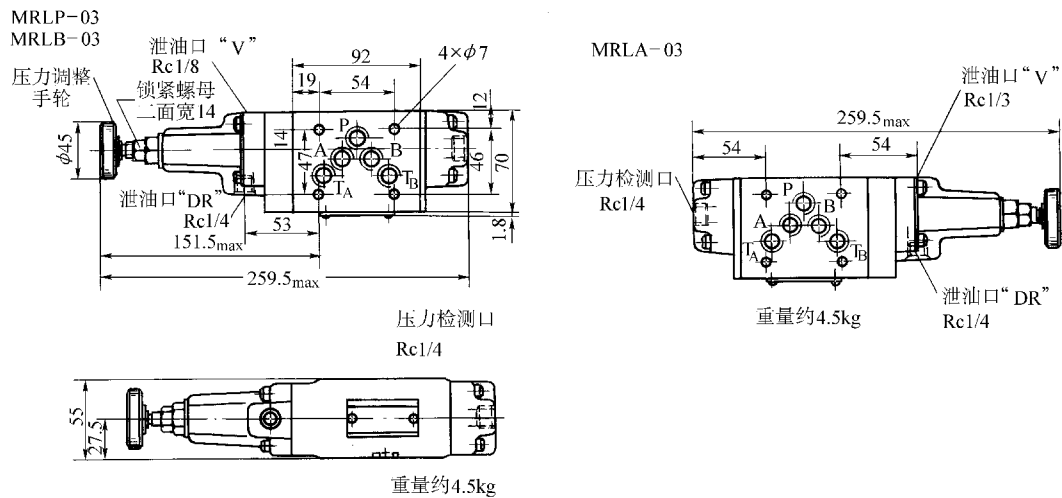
03 规格低压叠加减压阀外形尺寸图
